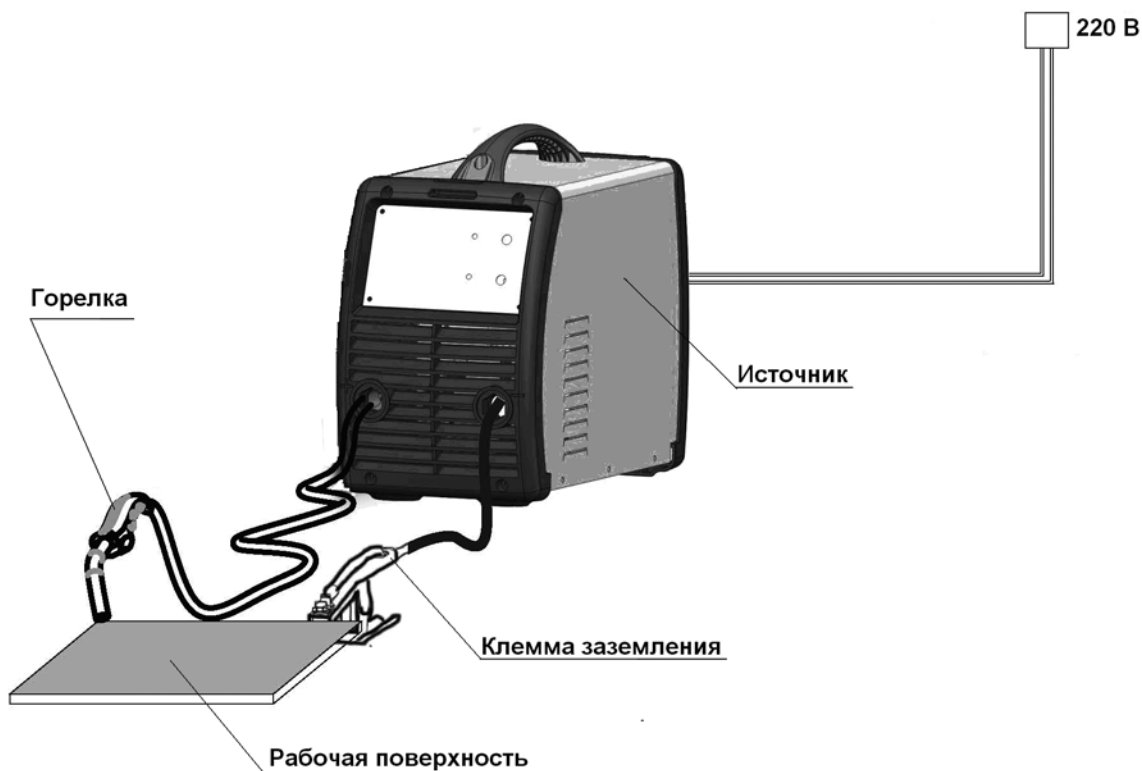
Схема подключения оборудования для механизированной сварки FCAW самозащитной порошковой проволокой FCAW.
